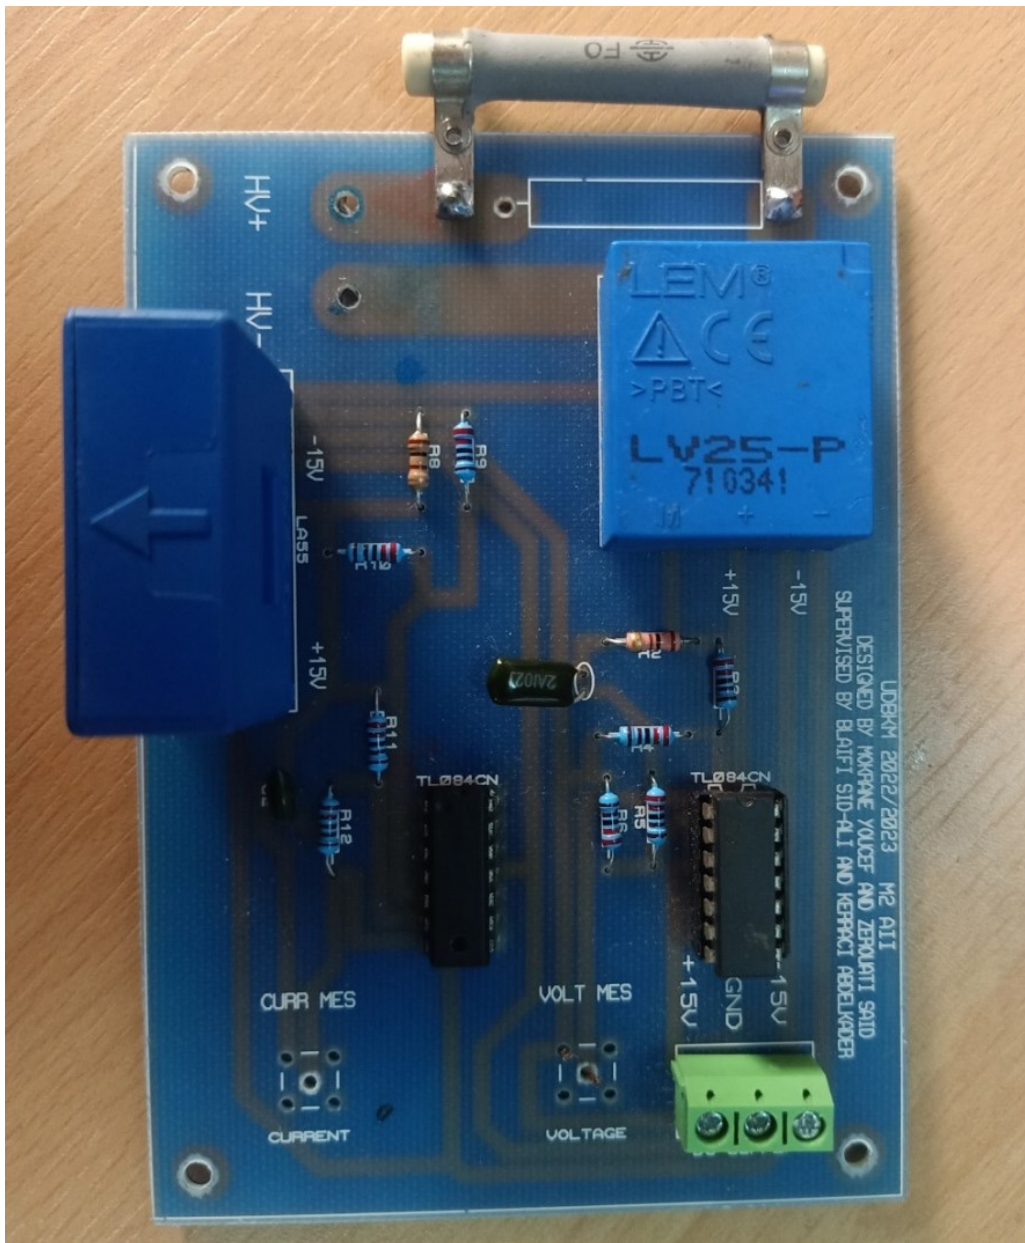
Photo réelle de la carte PCB de mesure
